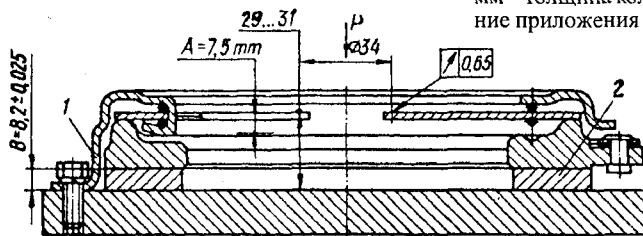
Контроль сцепления: 1 – кожух сцепления с нажимным диском; 2 – кольцо толщиной В= 8,2±0,025 мм; 3 – плита упорная; А= 7,5 мм – ход упорного фланца для полного выключения сцепления; Р – направление приложения усилия 1020 Н (102 кгс) на нажимную пружину на $\varnothing 34$ мм
